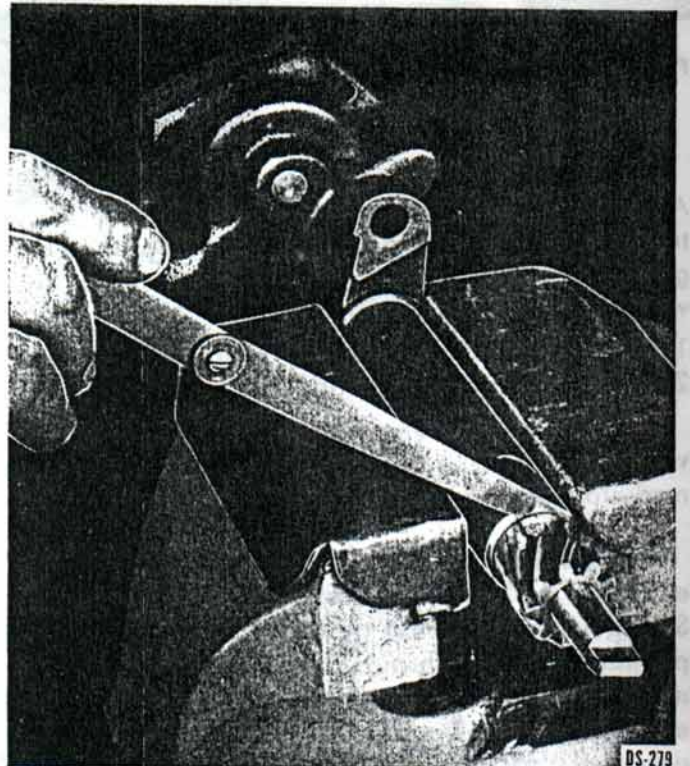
Verificando el juego libre entre cuerpo de bomba y engranaje helicoidal.
